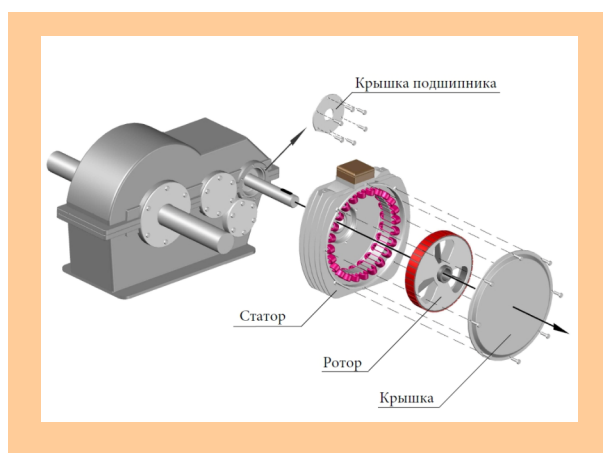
Основные элементы двигателя и схема его установки на редукторе
